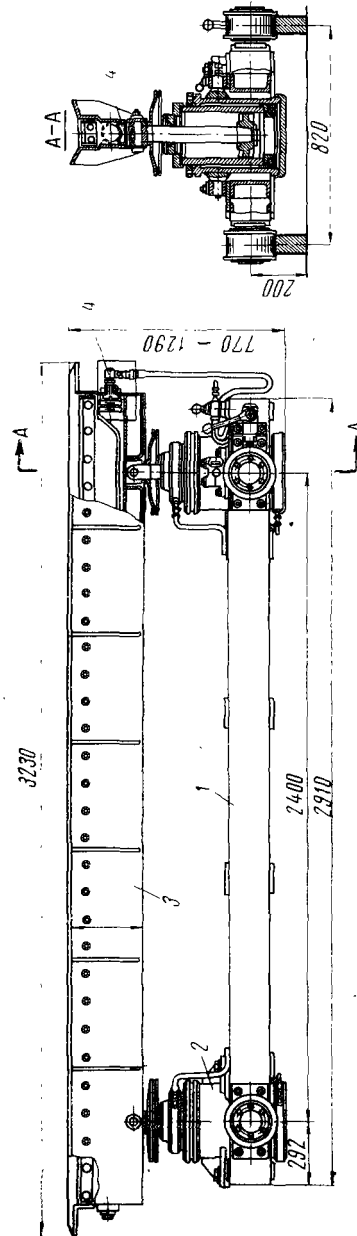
Флюсовая подушка для сварки продольных швов
